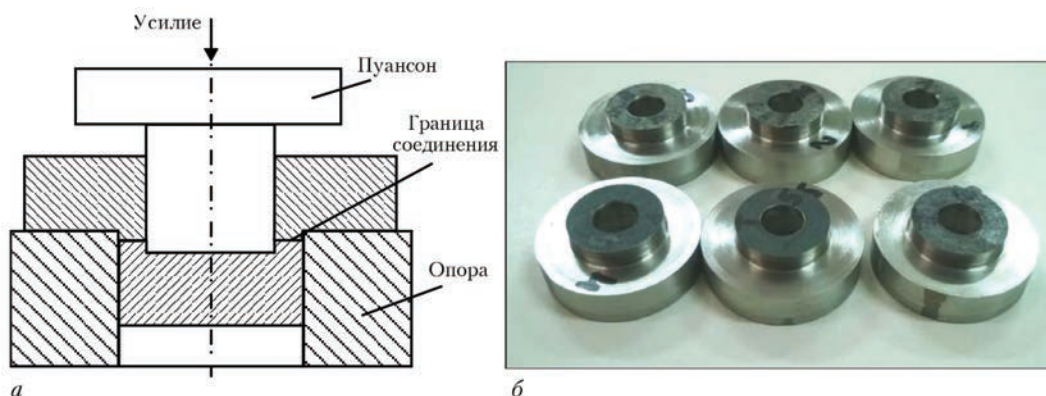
Схема испытания на отрыв слоев биметалла (а) и общий вид образцов (б)
